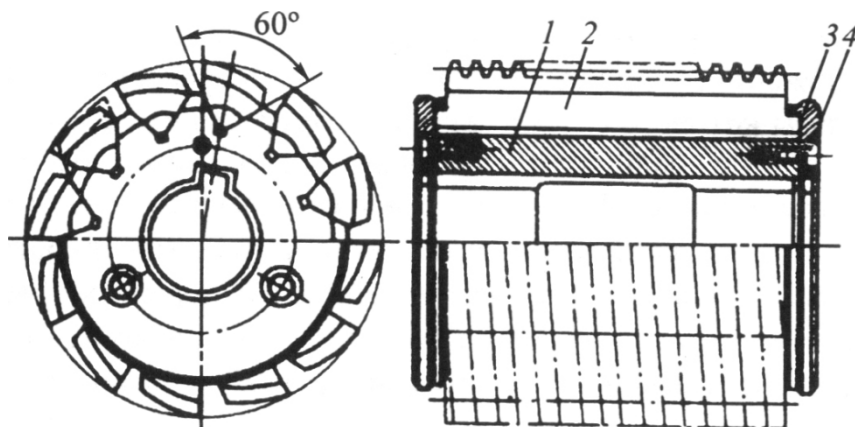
Сборная червячная фреза с поворотными рейками фирмы «Сампутенсили»
